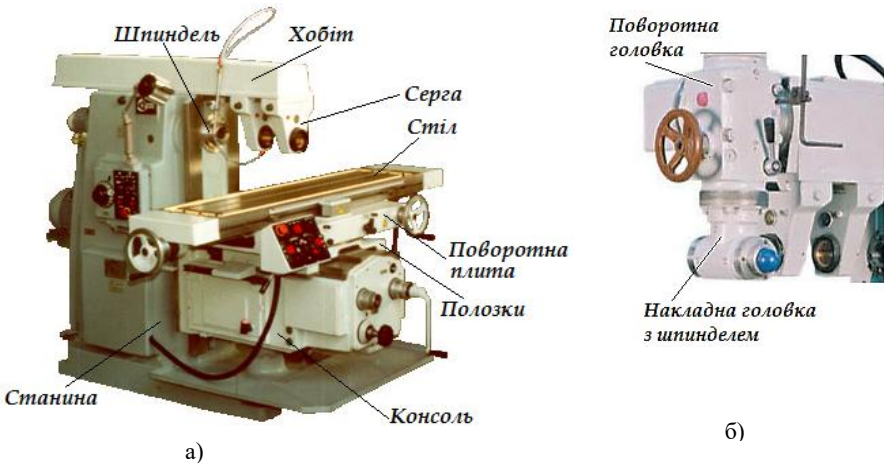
Горизонтальний консольно-фрезерний верстат
